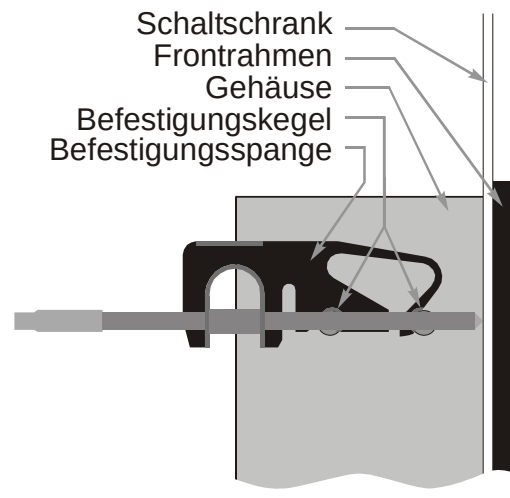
Seitenansicht - mit Befestigungsklammer
